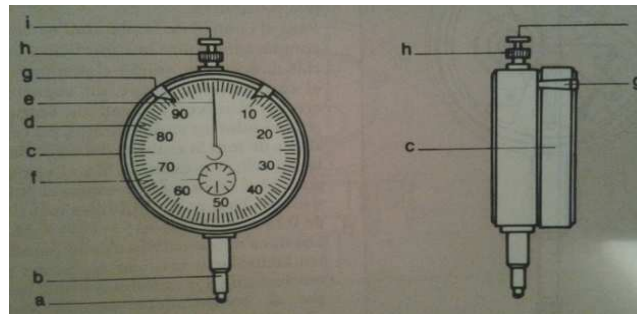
Partes fundamentales del comparador de carátula.
